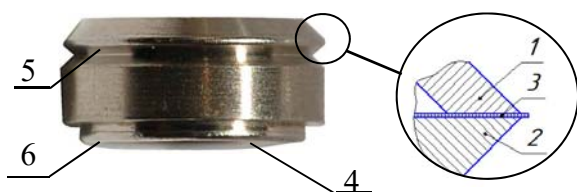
Внешний вид источник на основе Cu-244 и конструкция сварного соединения. 1- шайба, 2-корпус, 3- окно, 4- пробка, 5 - сварной шов №1, 6- сварной шов №2
